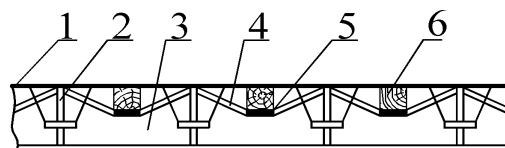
Подкрепление пластины за счёт установки упруго-пластической опоры: 1– обшивка; 2– шпангоут; 3– стрингер; 4– оттяжка; 5– полоса; 6– брус
